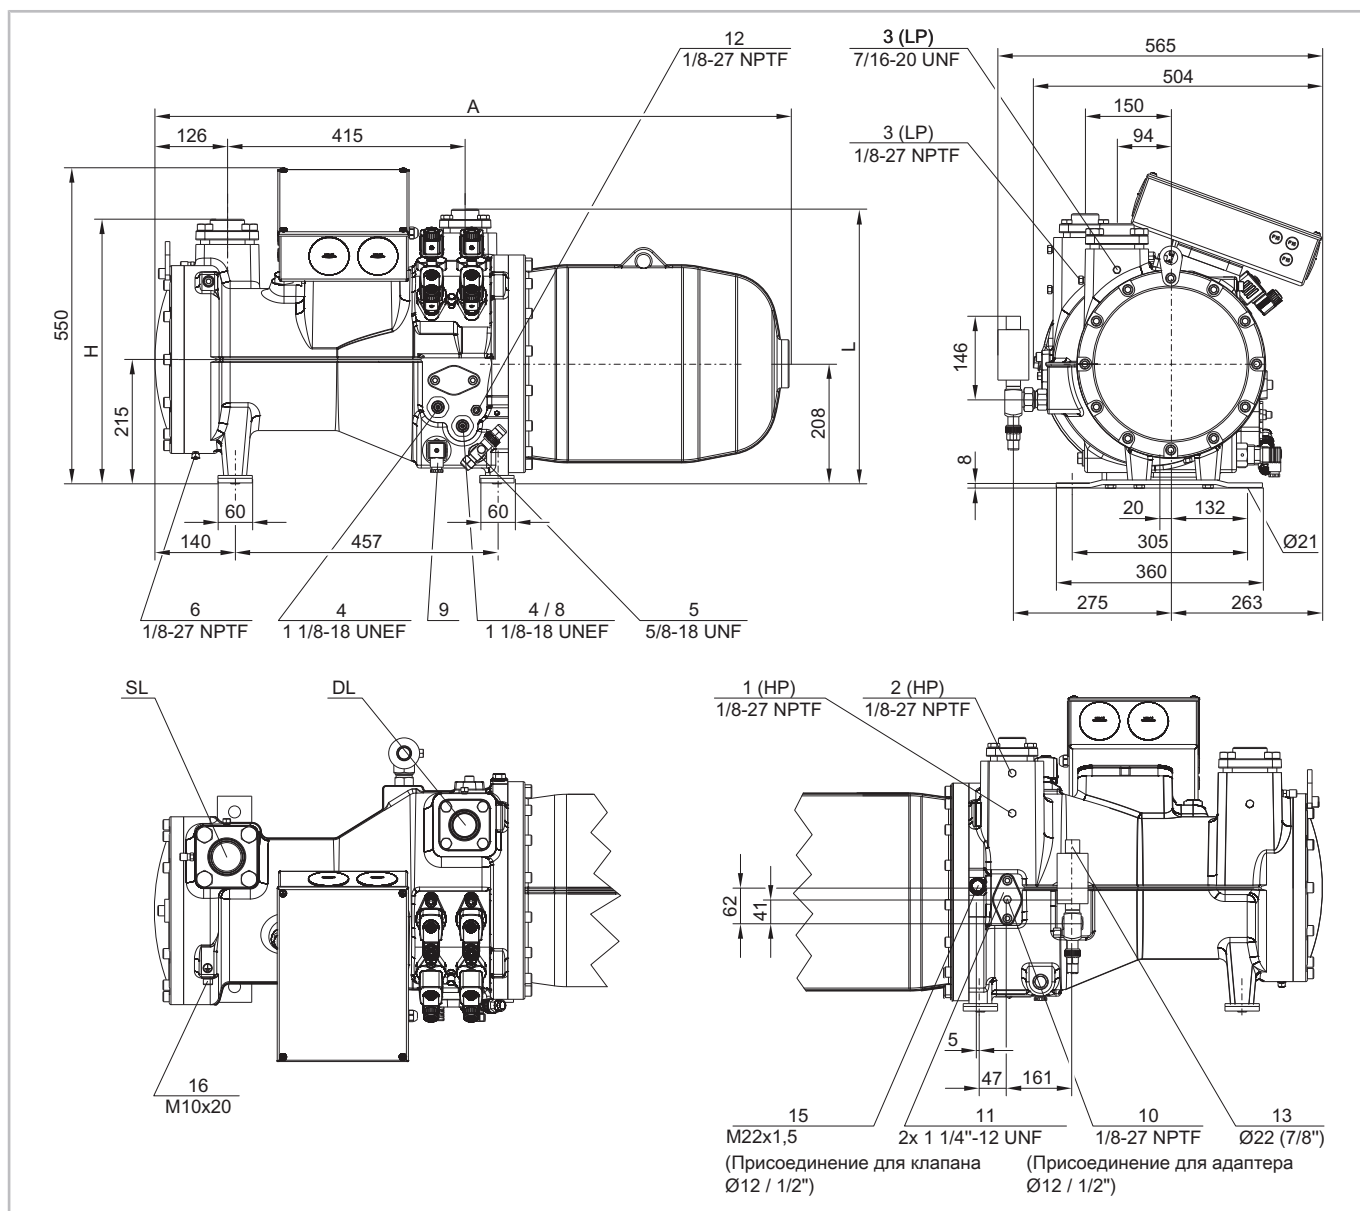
Чертежи с указанием размеров для CSH6553-35Y .. CSH6593-60Y, CSK6153-50 .. CSK6163-60
